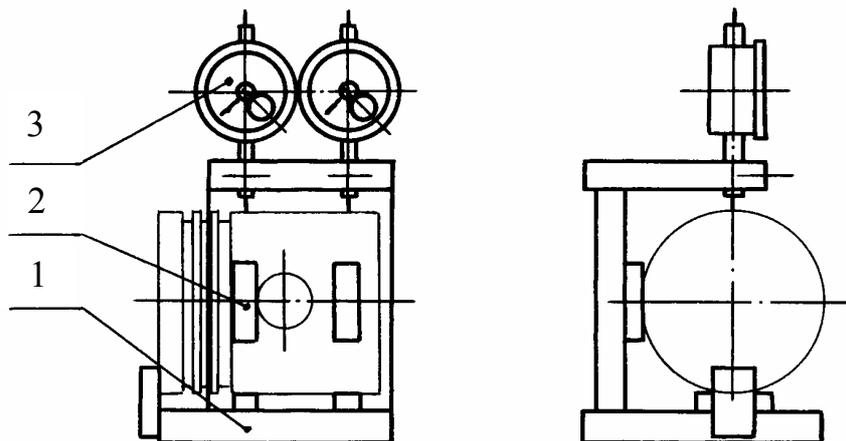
Прибор для измерения размеров, эллипсообразности и конусообразности юбки поршня: 1 – основание; 2 – опоры; 3 – индикаторные головки
